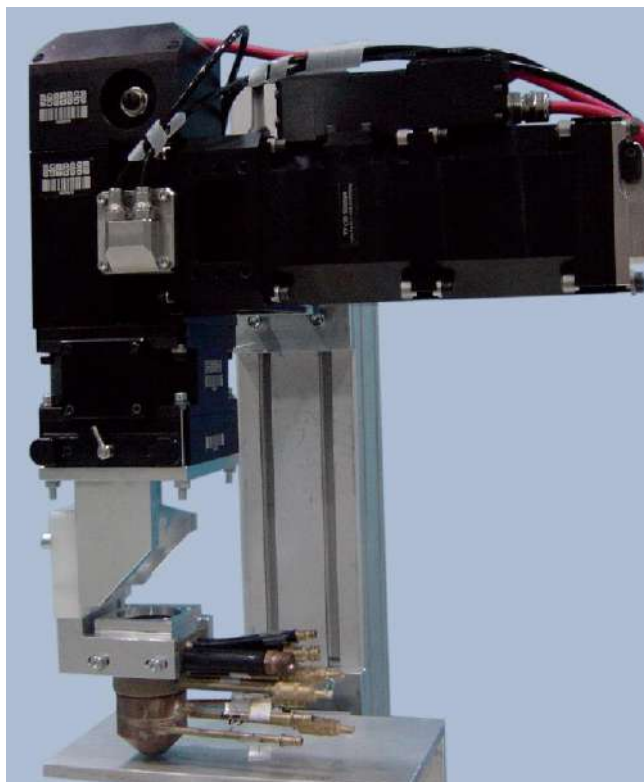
Інтегрована головка для лазерно-плазмового зварювання [89].
